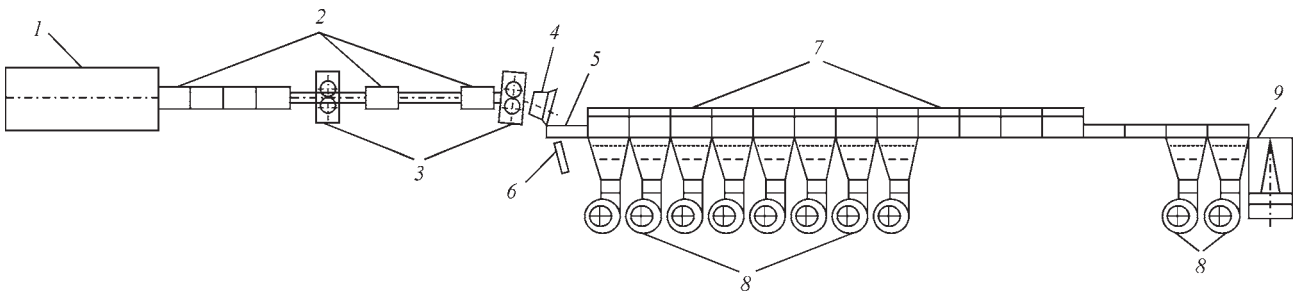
Схематичне розташування технологічного обладнання лінії Стелмор [1]: 1 – чистовий прокатний блок; 2 – ділянка водяного охолодження; 3 – трайбапарати; 4 – виткоутворювач; 5 – приймальний стіл витків прокату; 6 – пірометр; 7 – ділянка регульованого повітряного охолодження з роликівим транспортером і теплоізоляційними кришками; 8 – дуттьові повітряні вентиляторні системи; 9 – шахта збирання витків
